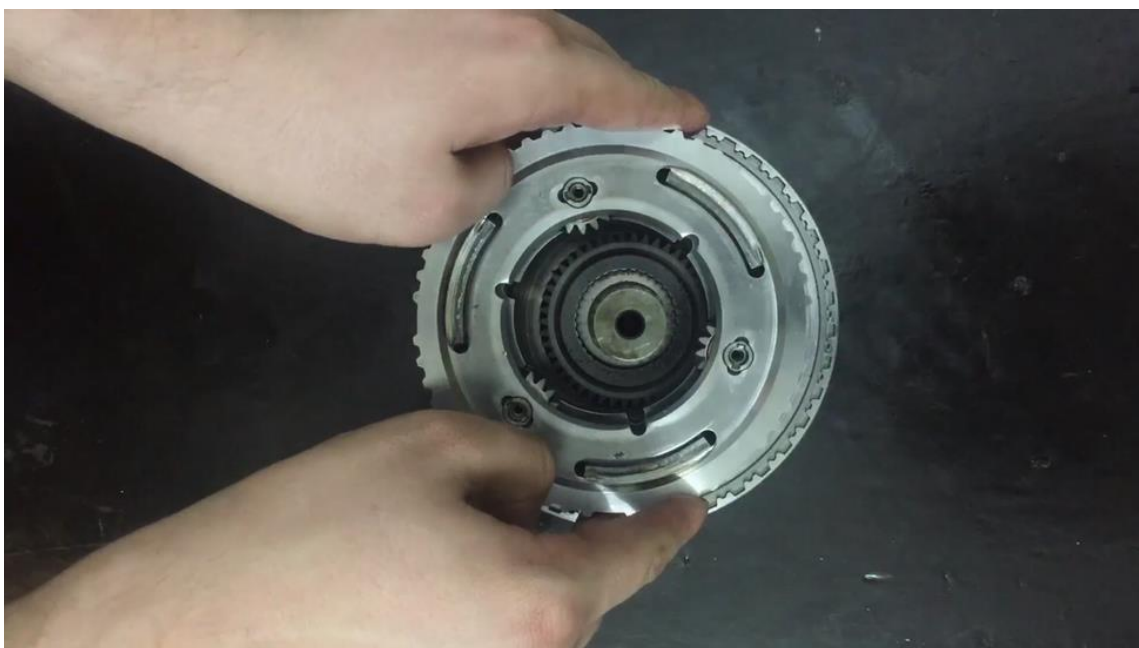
Сборка переднего планетарного редуктора с муфтами К1 и К3
